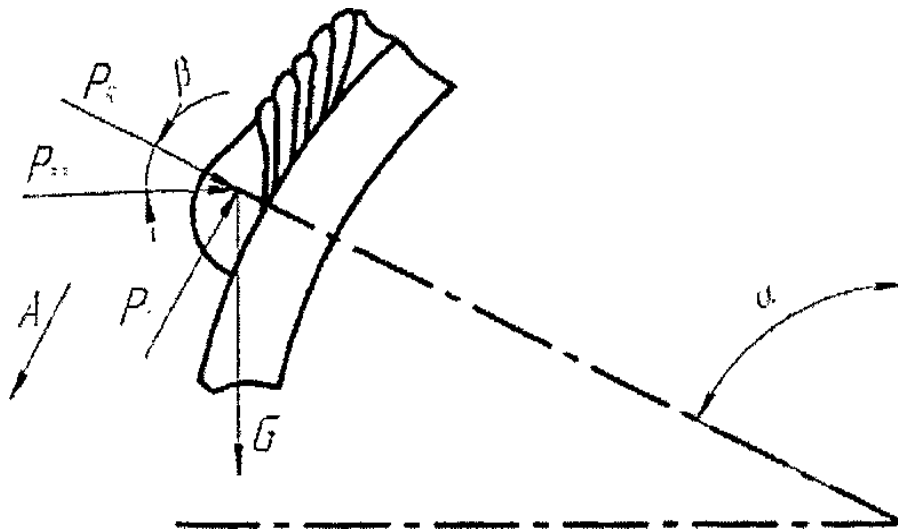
Схема сил действующая на сварочную ванну в положении от 0° - 90°
